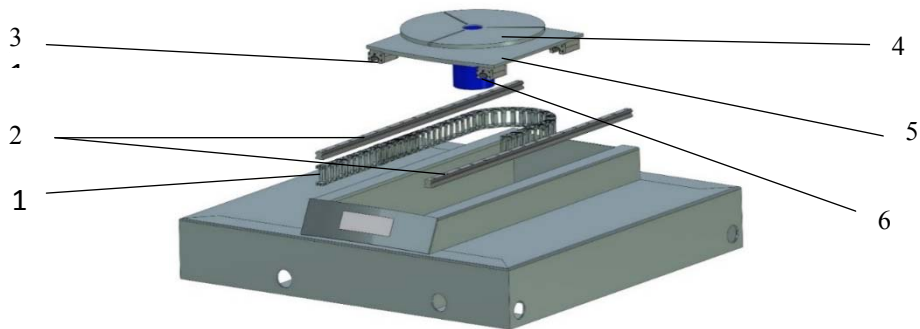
3D-модели элементов конструкции поворотного стола:
